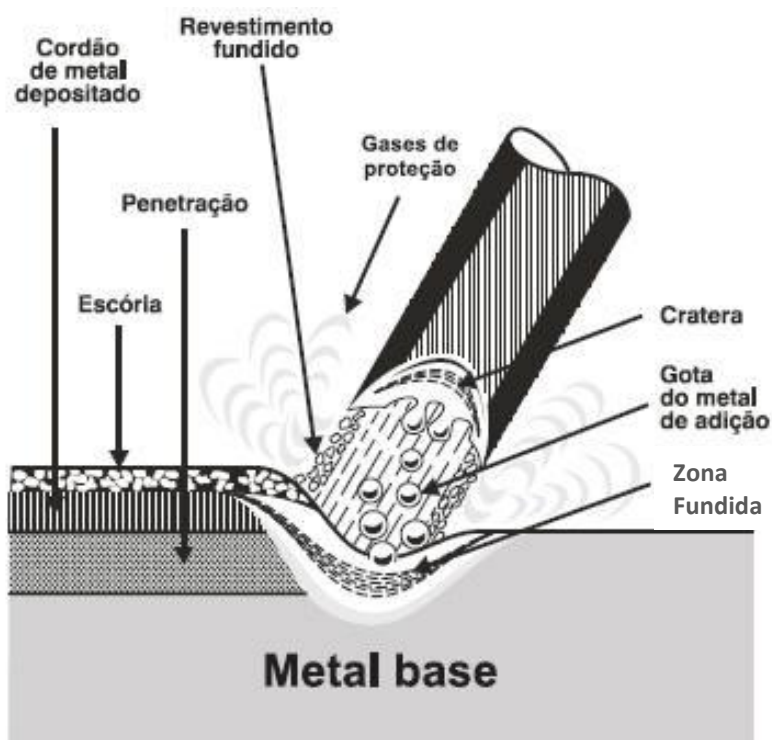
Ilustração do processo de soldadura por eletrodo revestido (fonte: oxigenio).
